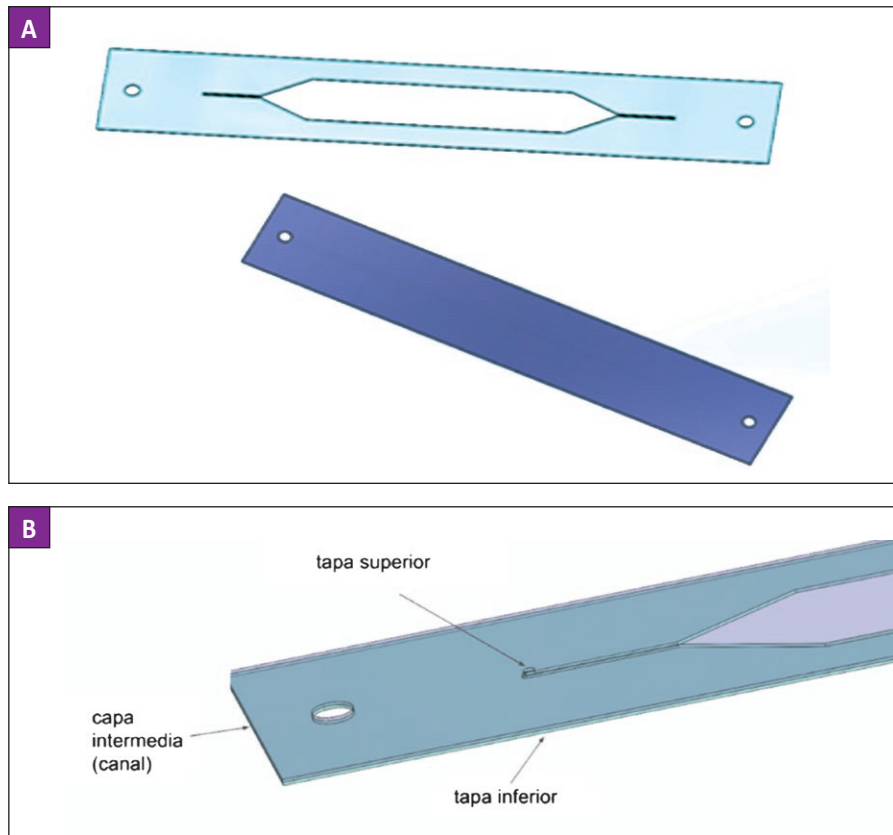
A. Partes del canal, capa intermedia e inferior. B. Diseño canal ensamblado. El canal es ensamblado fácilmente al dispositivo y es descartable para cada paciente.
